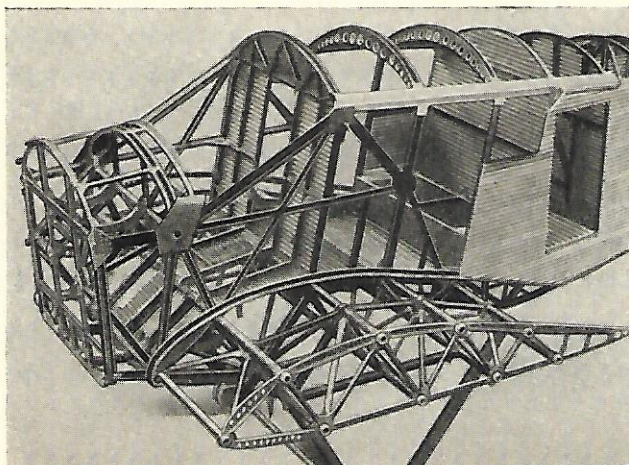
Rumpfaufbau der Junkers F 13 in Spantenbauweise
